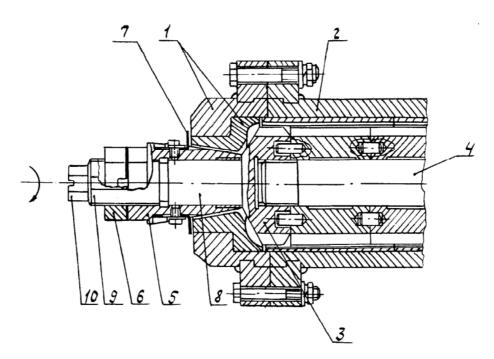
Выпускная головка экструдера для приготовления кормов по патенту РФ 2251363 [15]:
